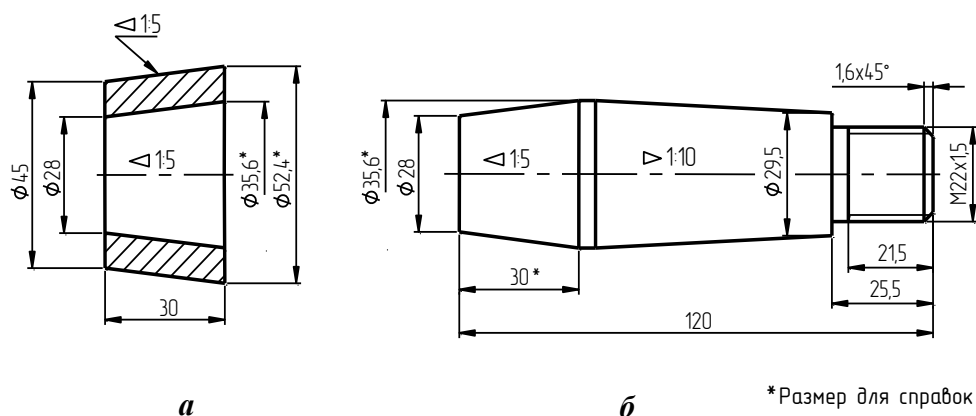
Правила применения знака «Конусность» при нанесении размеров конических поверхностей: а – охватывающая деталь (втулка);
